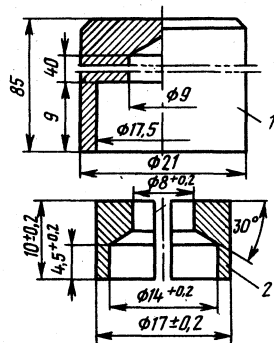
Приспособление для напрессовки маслоотражательных колпачков:
